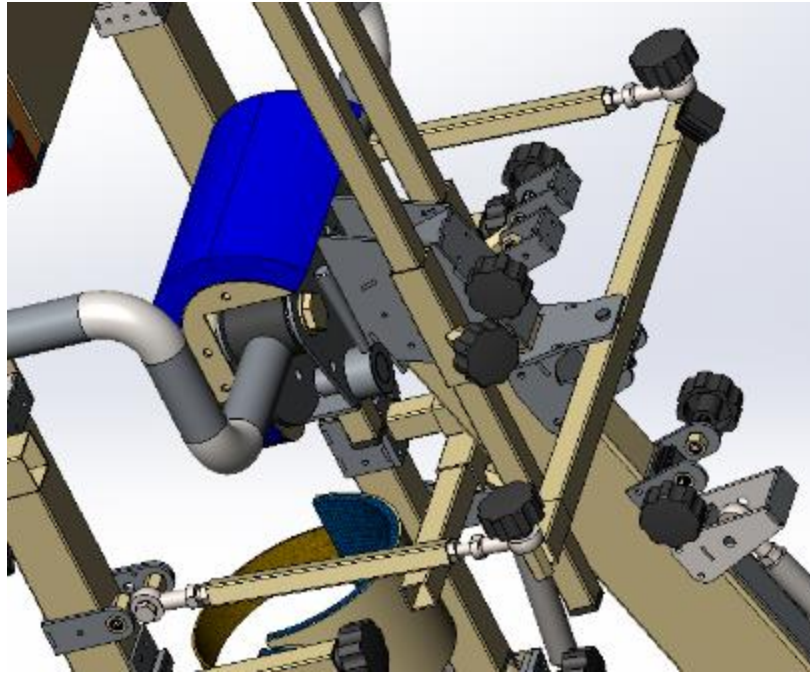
Трехмерная модель стабилизатора и площадки закрепления
